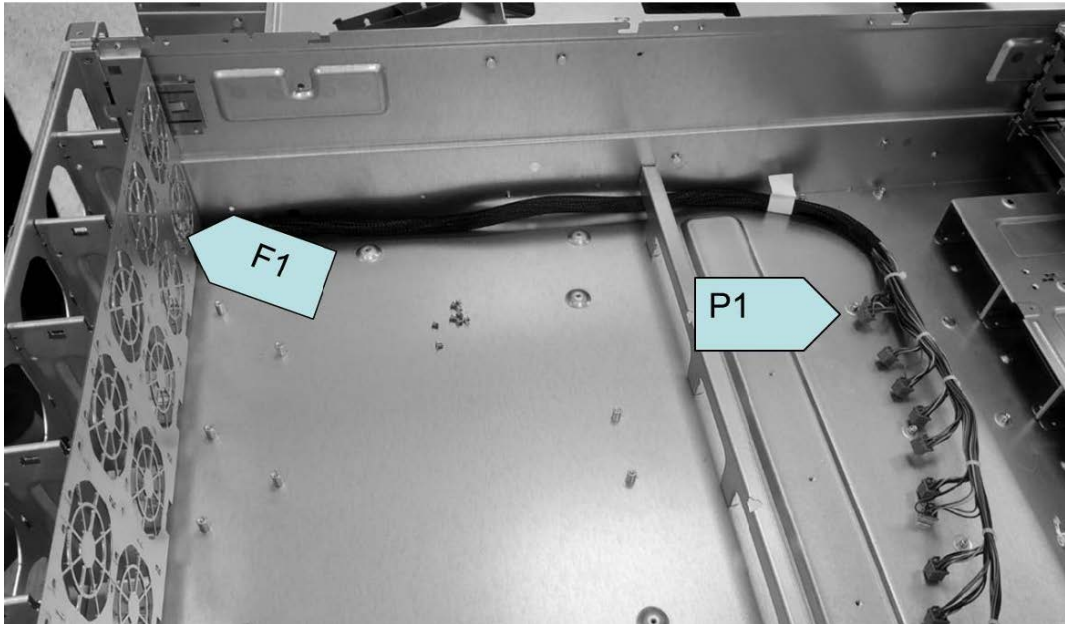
Assemblage du câble de ventilateur vers le support de ventilateur
